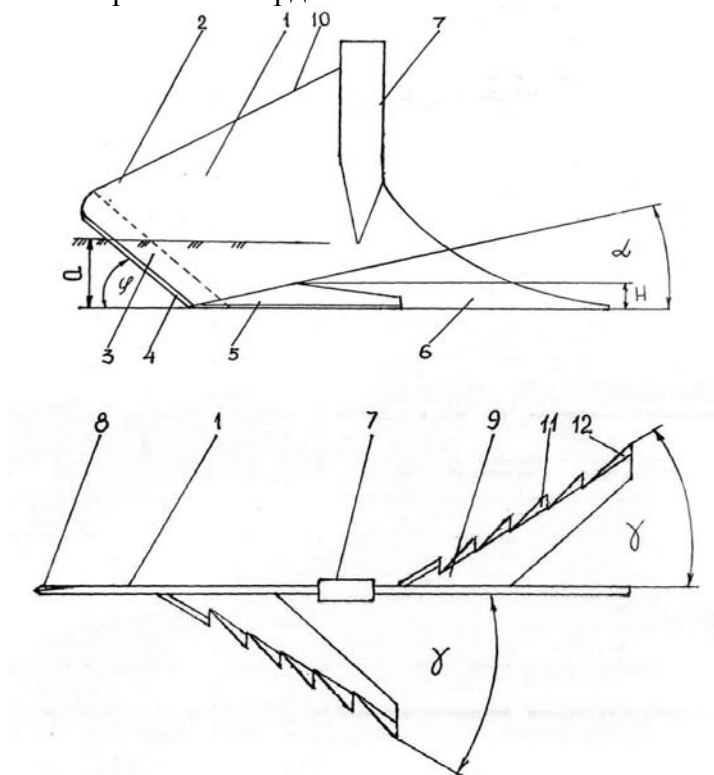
Рабочий орган с зубчатыми полулапами
